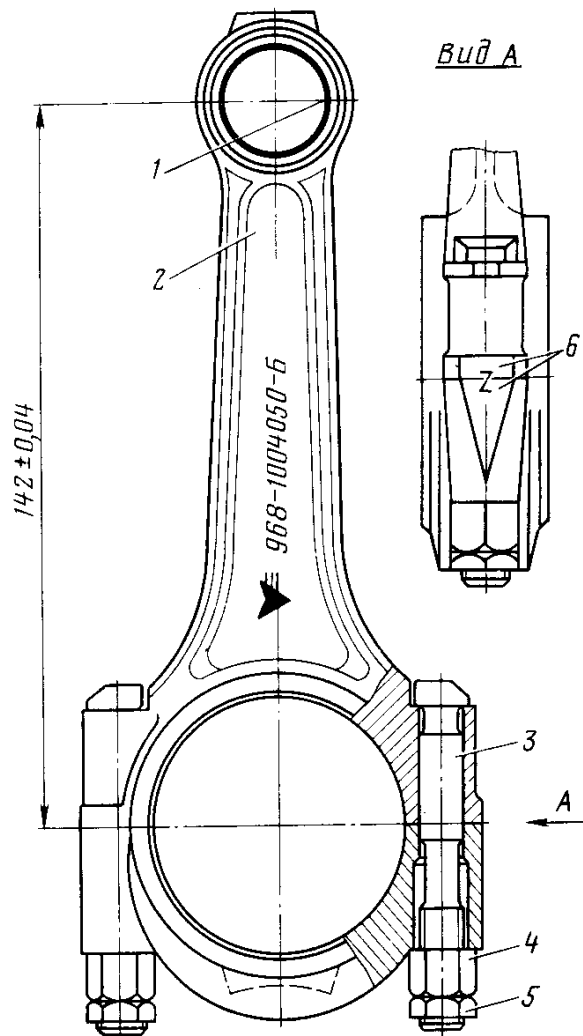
Шатун в сборе: 1 — стык втулки верхней головки шатуна; 2 — место цветового индекса размерной группы верхней головки шатуна; 3 — болт крепления крышки шатуна; 4 — гайка болта крышки шатуна; 5 — стопорная гайка; 6 — метка номера цилиндра
